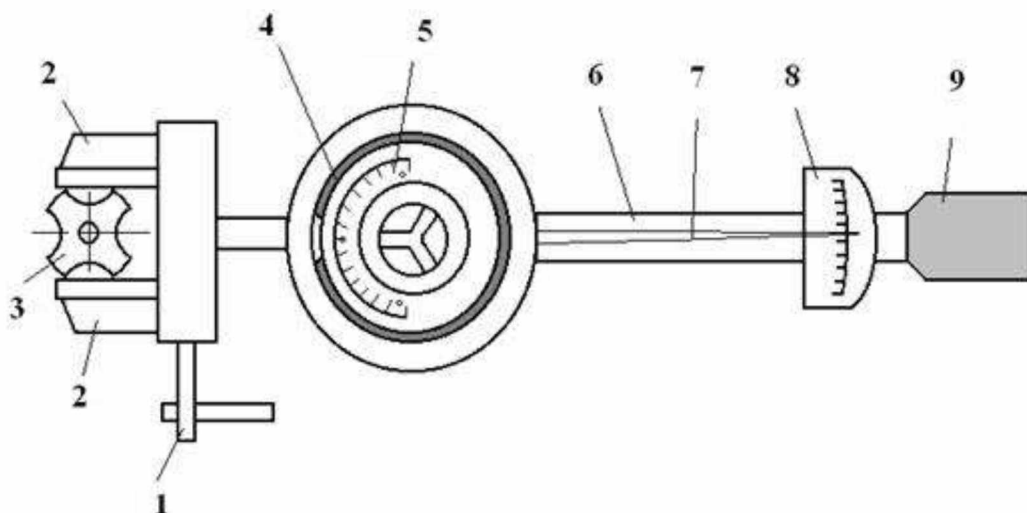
Прилад КИ-4832 для вимірювання бокового зазору в механізмах трансмісії
